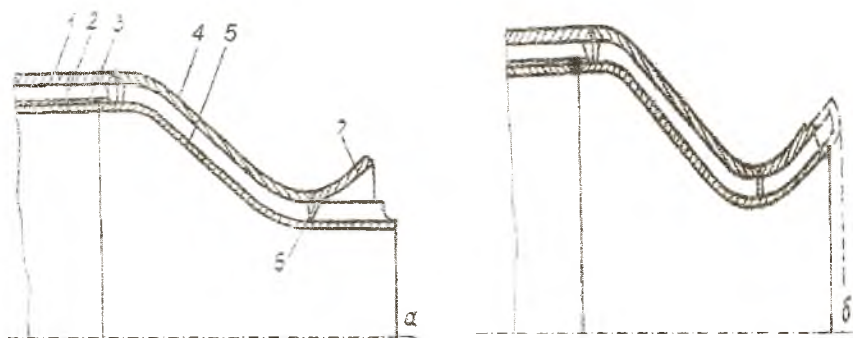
Положение деталей рубашки и стенки средней части корпуса камеры до (а) и после (б) развальцовки цилиндрического участка стенки: 1, 2, 3 – рубашка, гофрированная проставка и стенка цилиндрического участка корпуса; 4, 5 – рубашка и стенка входной части сопла, 6 – кольцевая проточка в ребрах; 7 – рубашка начального участка расширяющейся части сопла
